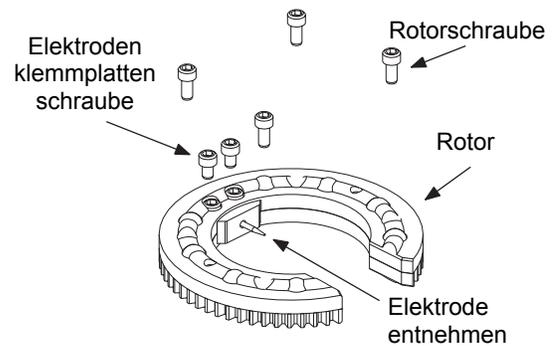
Rotor- und die Elektrodenklemmplattenschrauben entfernen
